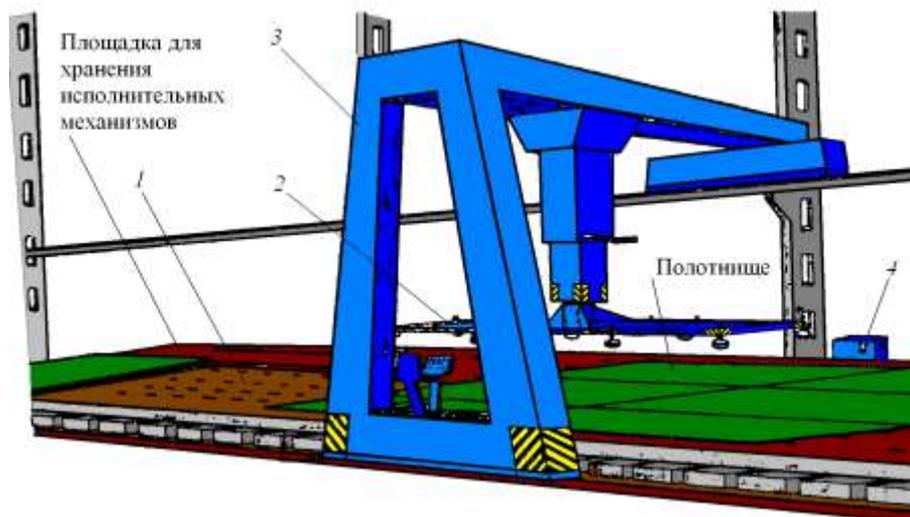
Общий вид многофункционального сборочно-сварочного манипулятора для изготовления плоских секций:
